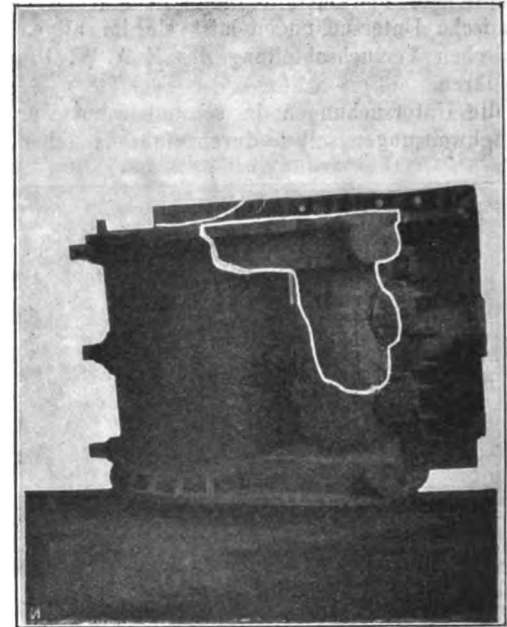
Lokomotivzylinder, geschweißt.
